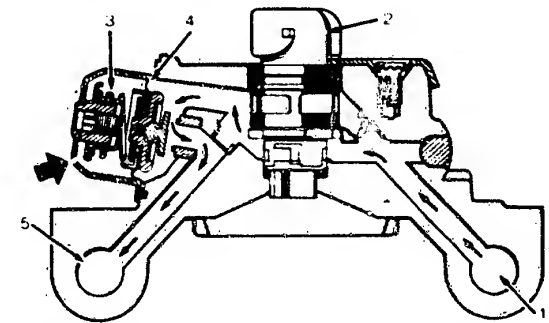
Schnitt durch den Einspritzgehäuse-Oberteil mit dem Druckregler: 1 Benzineinlassbohrung – 2 Einspritzventil – 3 Druckfeder – 4 Membrane – 5 Rücklaufleitung.
